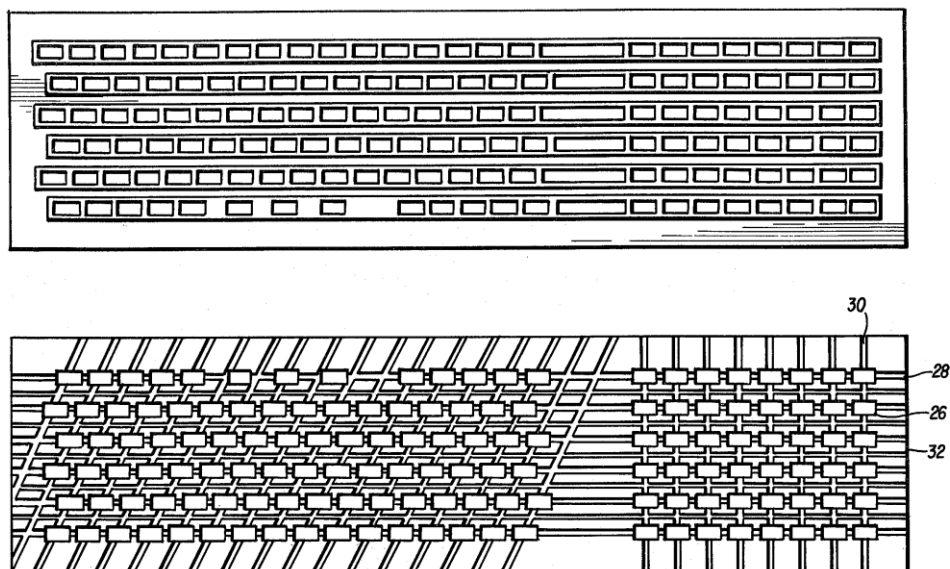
Вид корпуса клавиатуры сверху и снизу
